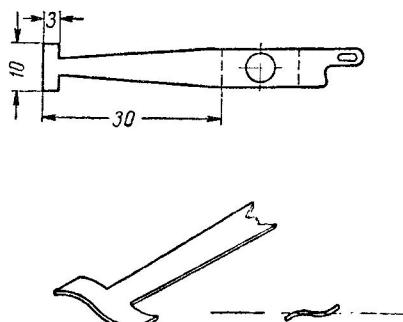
Верхний контакт автостопа (рис. 1, деталь 6)
